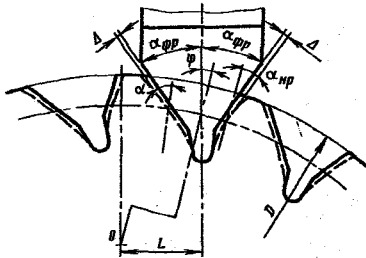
Станочное закрепление дисковой фрезы определенной установки с заготовкой зубчатого колеса, имеющего несимметричные профили и поднутренные основания зубьев
